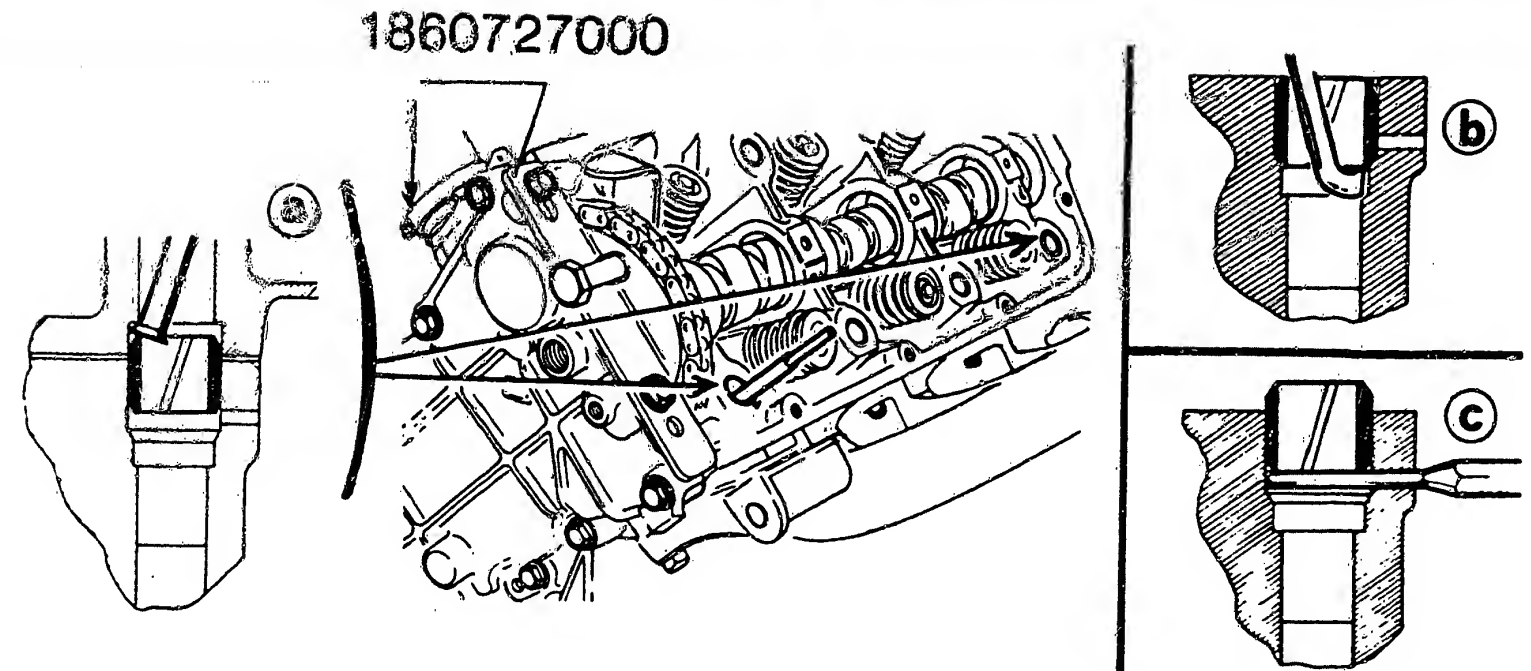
2850 V6-Motor: Das Nockenwellen-Steuerrad ist vor dem Ausbau des Zylinderkopfs mit dem Spezialwerkzeug 186072000 zu fixieren, damit die Kette gespannt bleibt. a) Die beiden Zentrierhülsen sind vor dem Ausbau abzusenken, und vor dem Einbau wieder anzuheben (b) und zu sichern (c).
